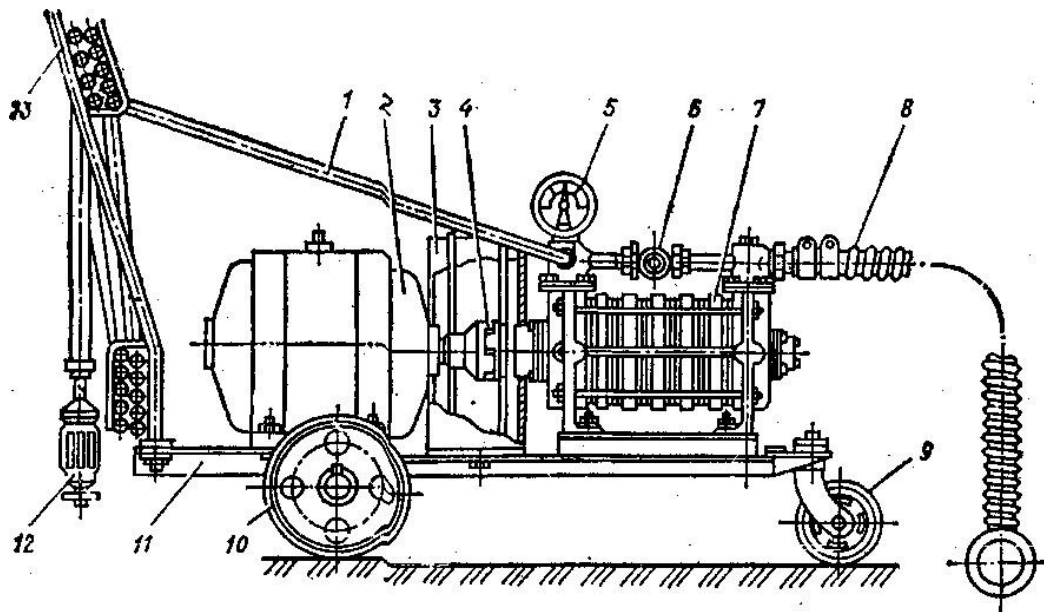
Робоче креслення установки 5BCm-1500 для миття автомобіля:
